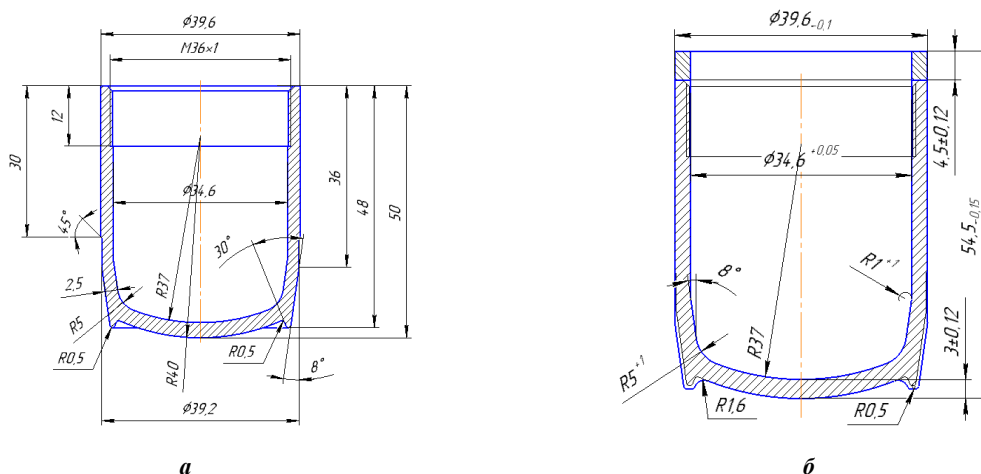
а - креслення деталі; б – креслення деталі з припуском на обрізування
